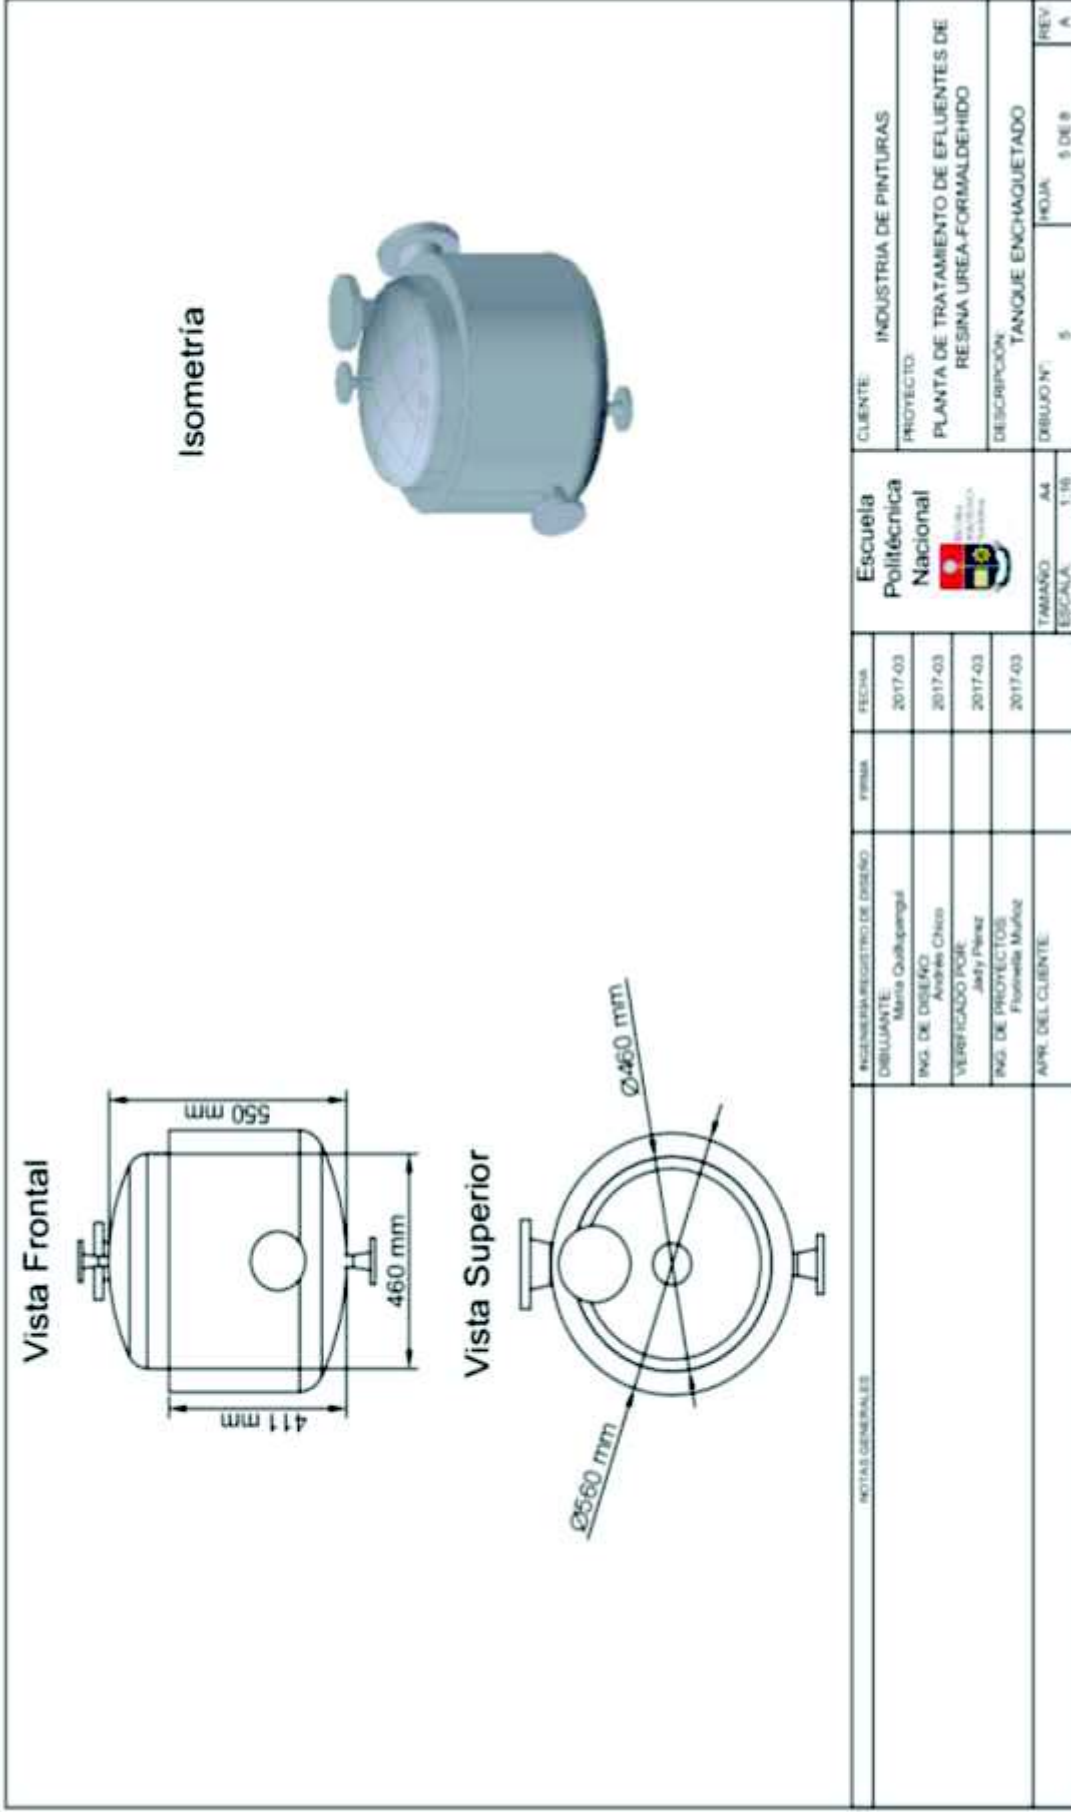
Plano de elevación del tanque de acondicionamiento enchaquetado
